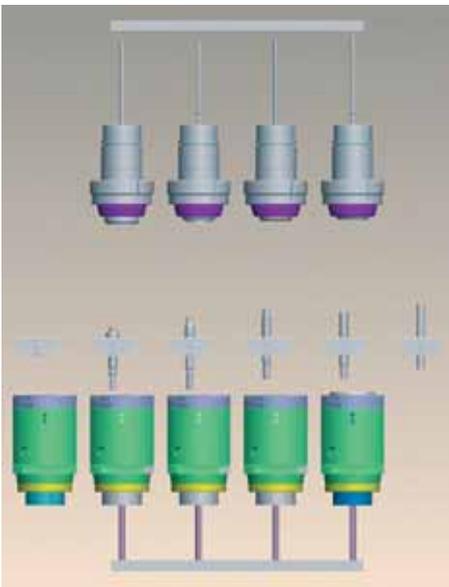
CAD-Daten der Werkzeug- und Maschinenelemente.
